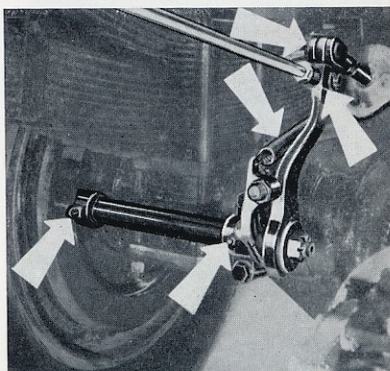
Levier de commande de frein arrière et graissage des chapes, sur pont arrière P 371.
